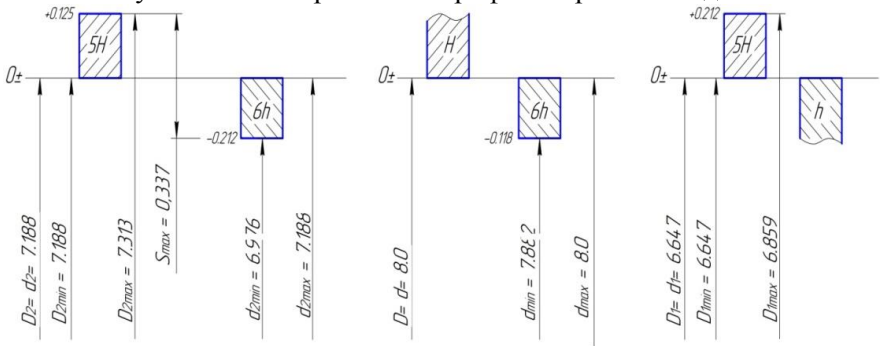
Схеми розташування полів допусків нарізного з'єднання
